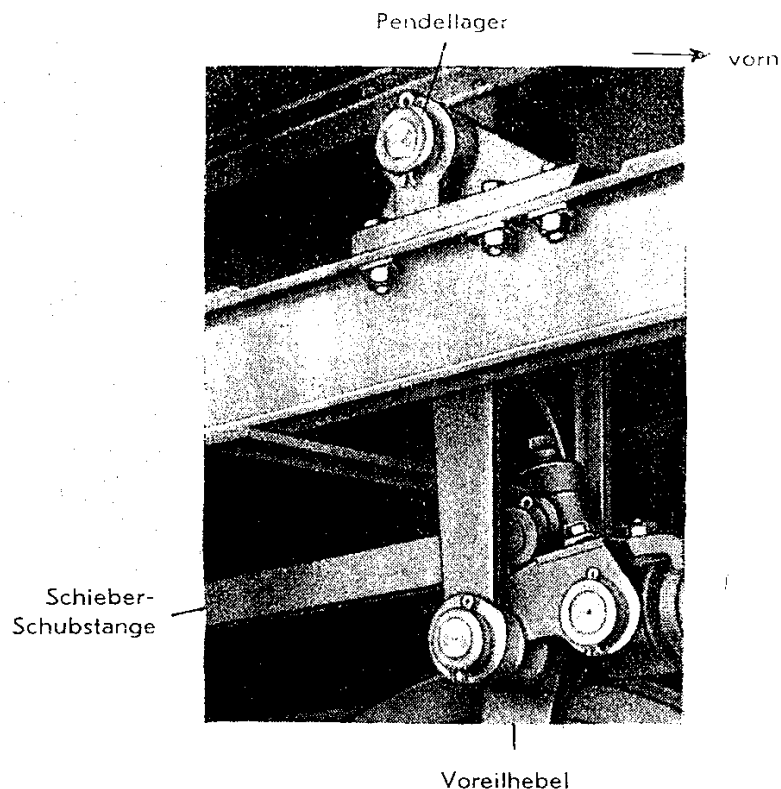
Hintere Schieberstangenführung mit Pendelaufhängung
